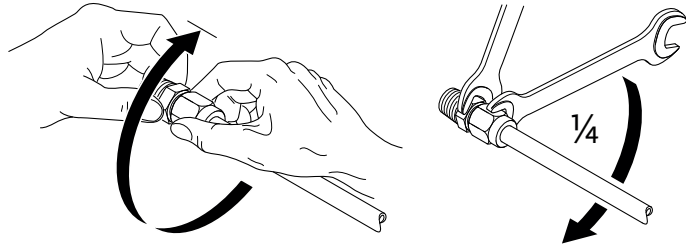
Допълнително завъртане на компресионния фитинг с 1/4 оборот
